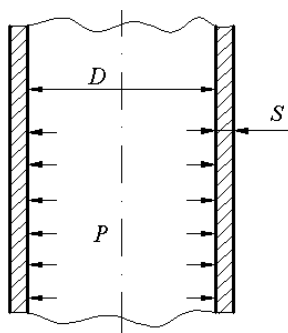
Розрахункова схема циліндричної обичайки
